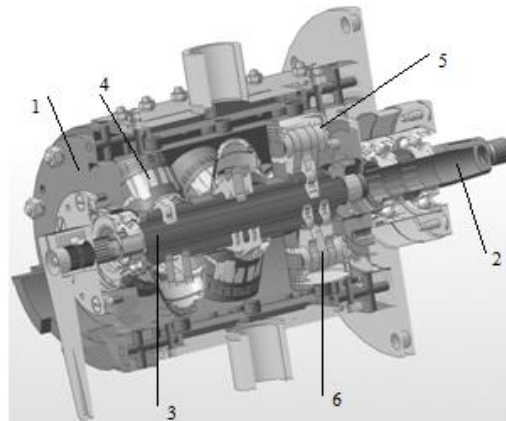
Роторно-поршковий двигун 12РПД-4,4/1,75 [6]:
